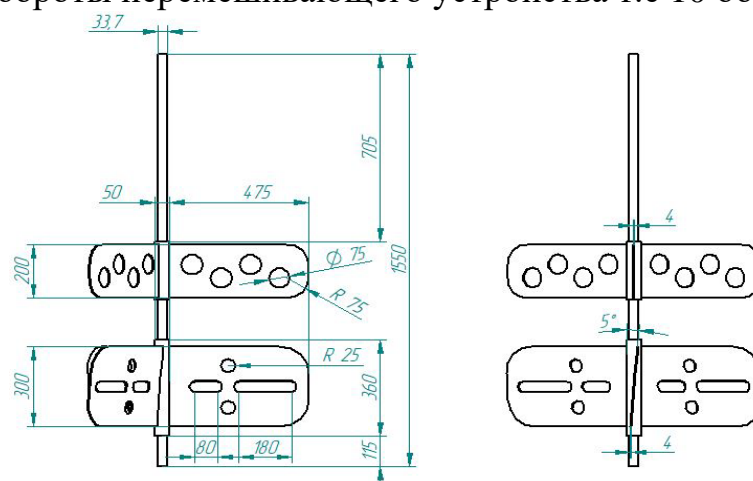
Перемешивающее устройство для резервуара ОСВ-1
